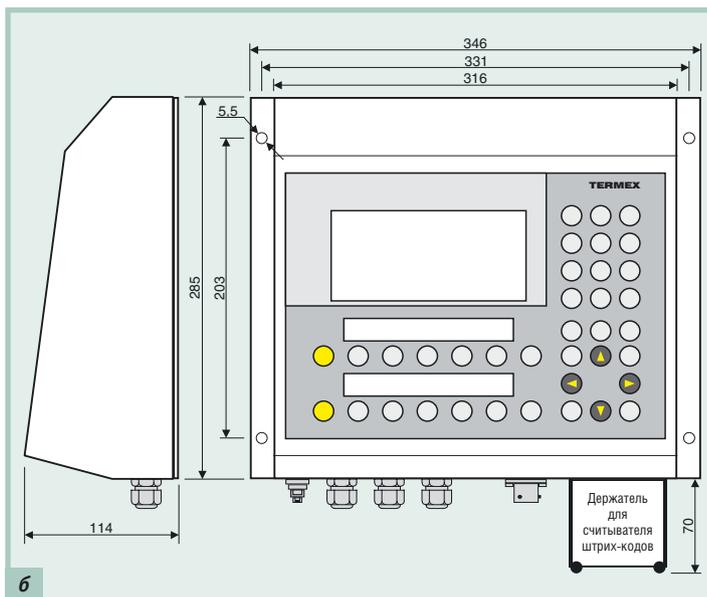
Внешний вид конструкции блока панели TERMEK и различных монтажных корпусов:
